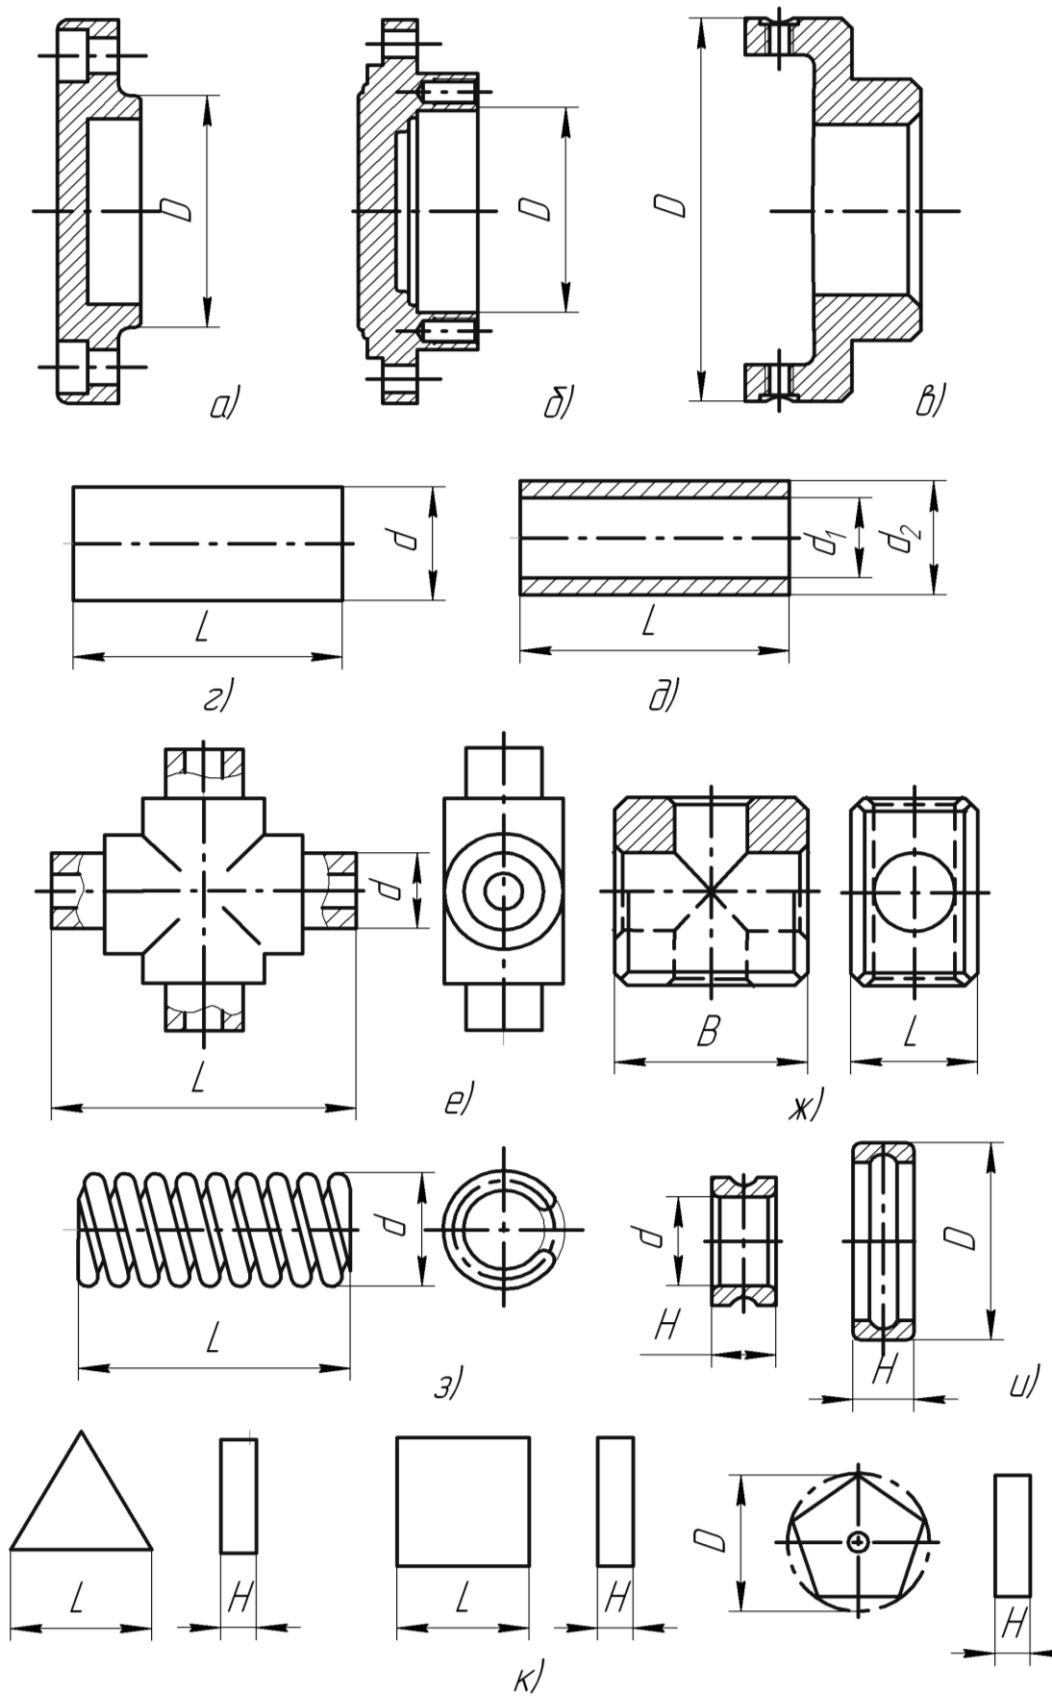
Детали с торцевыми рабочими поверхностями
